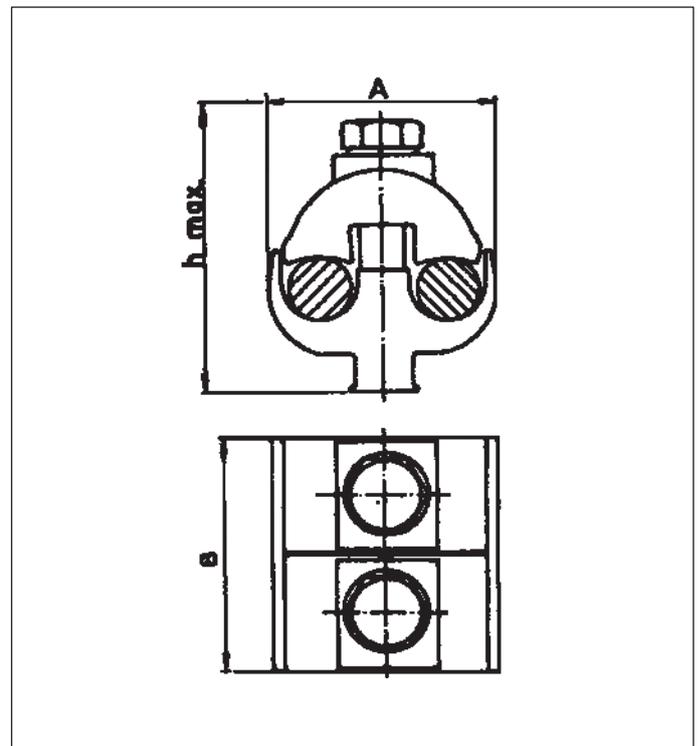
Конструкция контактного зажима: корпус из алюминиевого сплава и болты из защищенной стали.
